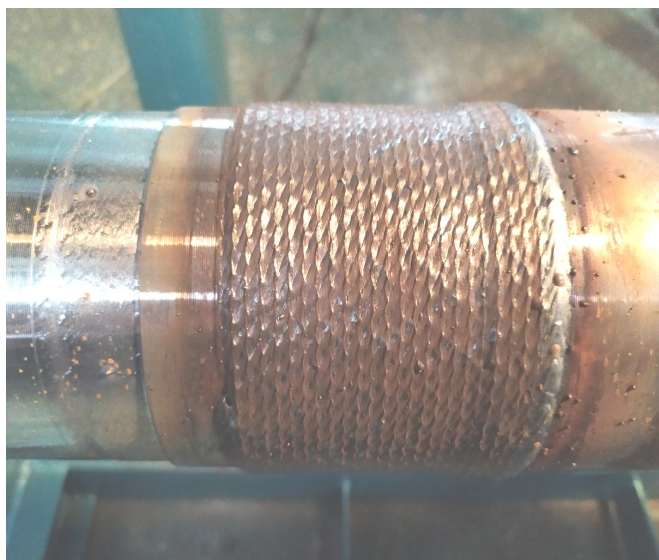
Фрагмент вала ротора с поверхностью, наплавленной на установке РМ-17
